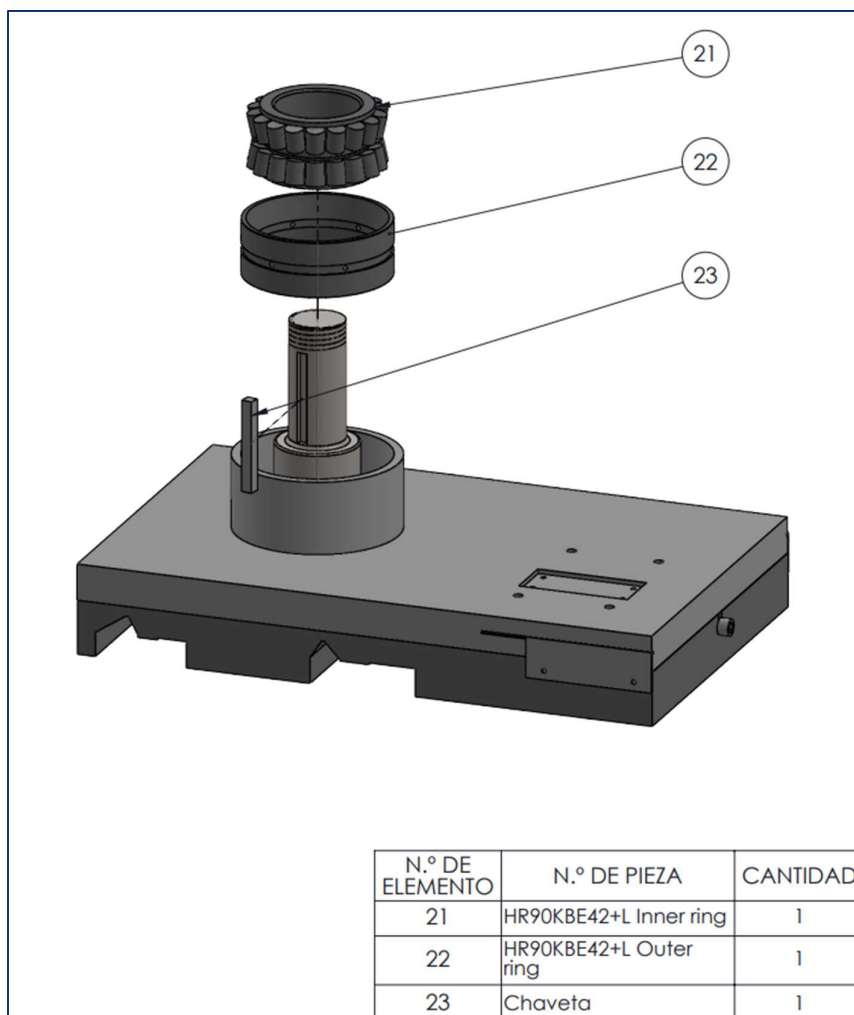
ensamble base adaptable a torno con caja de rodamientos, rodamientos cónicos simple y doble, eje y chaveta.
